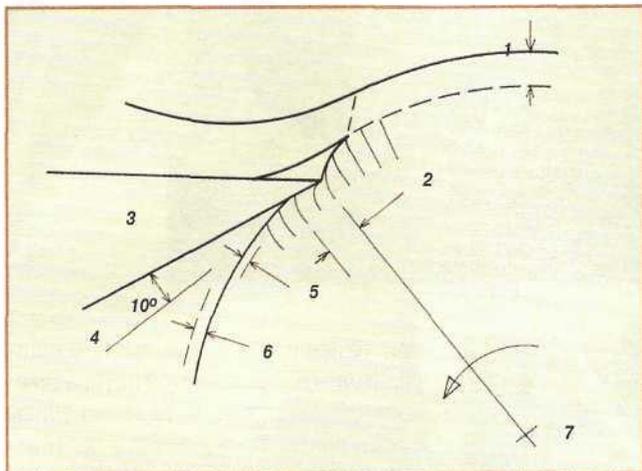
Схема обдирки заготовки: 1 - глубина резания; 2 - связь опорырежущей кромки; 3 - лезвие инструмента; 4 - касательная; 5 - упругая деформация; 6 - пластическая деформация; 7 - ось станка.
